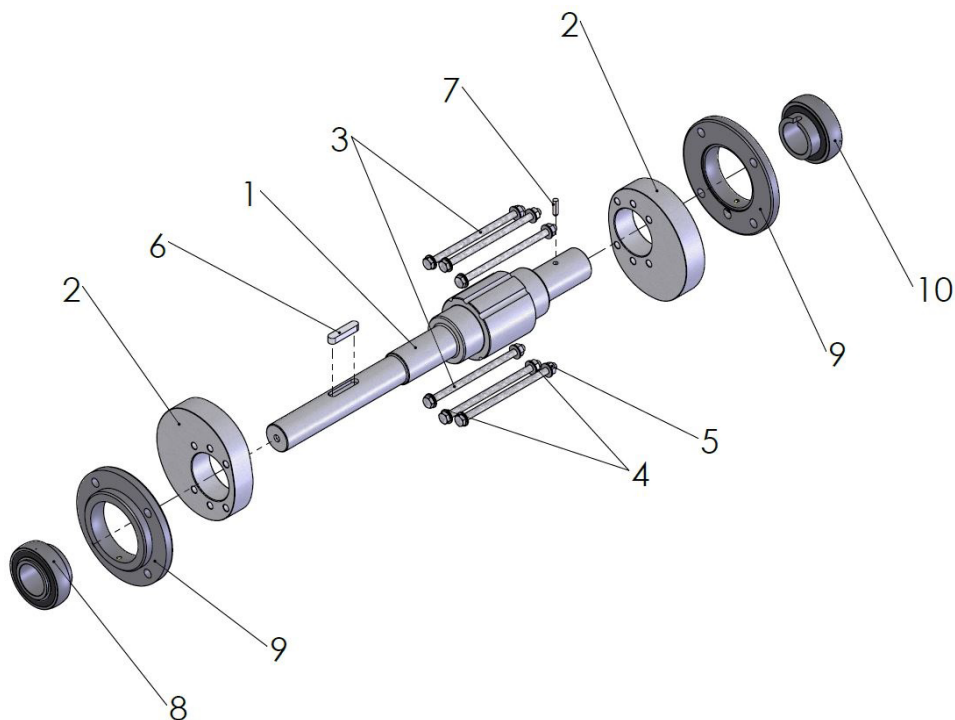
Vue éclatée du dispositif d'entraînement
